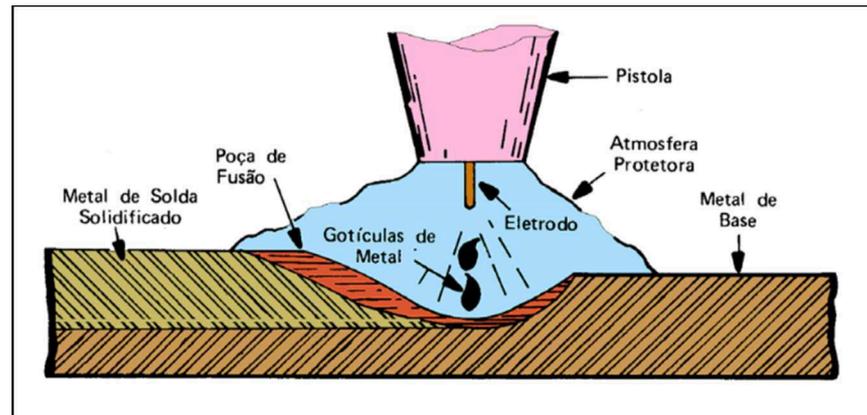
Processo de Soldagem - GMAW (FBTS, 2018).
